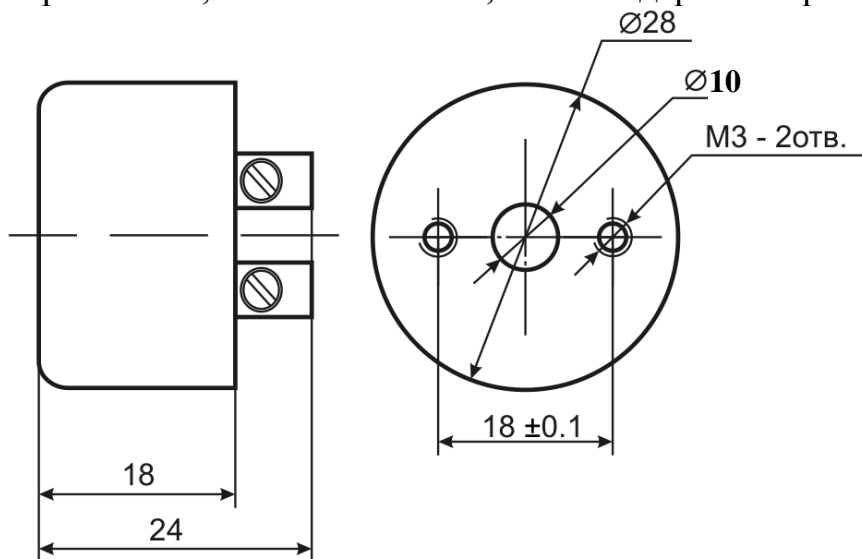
Общий вид, габаритные и посадочные размеры индикатора срабатывания ИС-1
